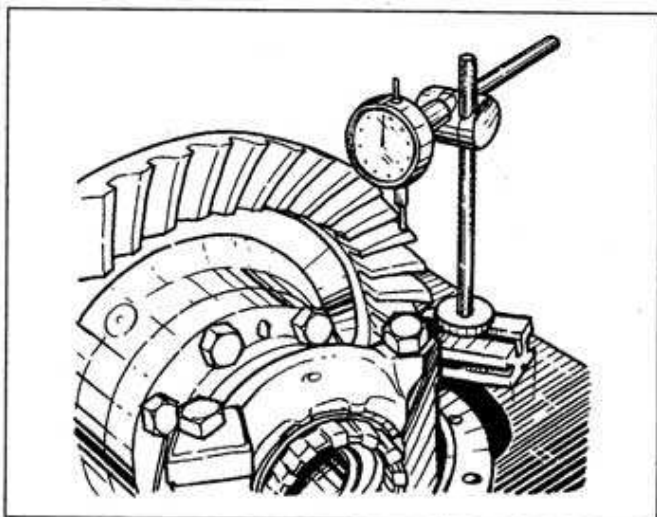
Проверка бокового зазора в зацеплении зубьев шестерен главной передачи (мост с балкой типа банджо)
